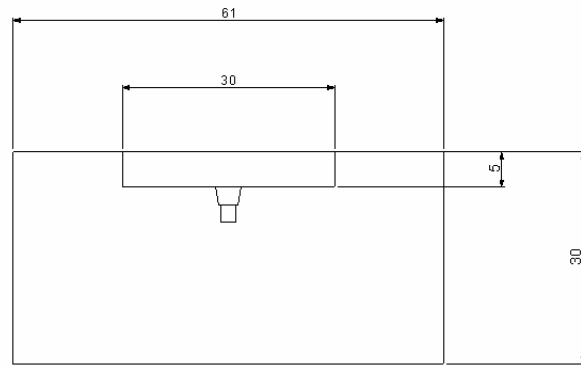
Dimensioni del supporto in millimetri, vista frontale
